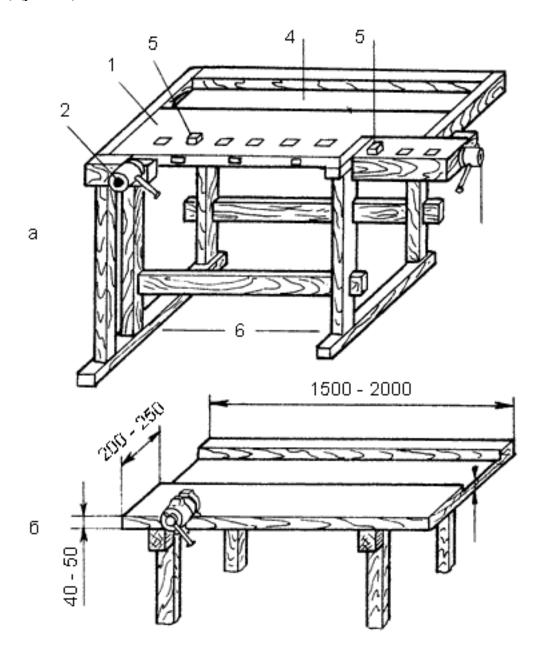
Рабочее место: a-столярный верстак; b-верстачная доска со съемными тисками; 1-верстачная доска; 2- передние тиски; 3-задние тиски; 4-лоток; 5-клиновой упор; b-подверстачье
